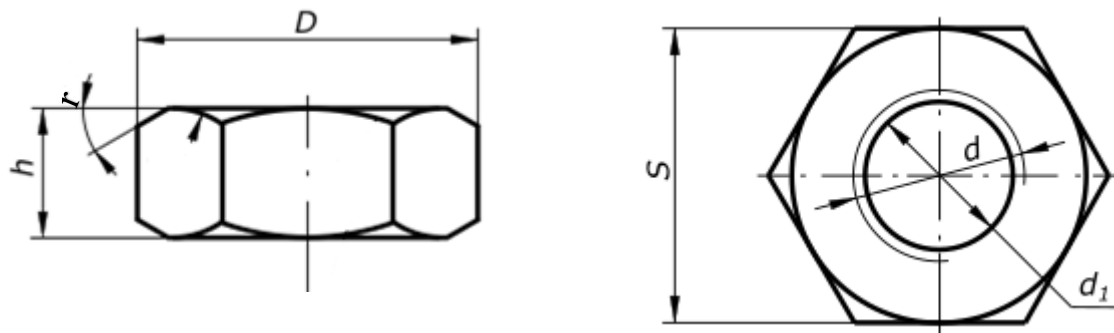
Чертеж гайки с привязкой габаритов
